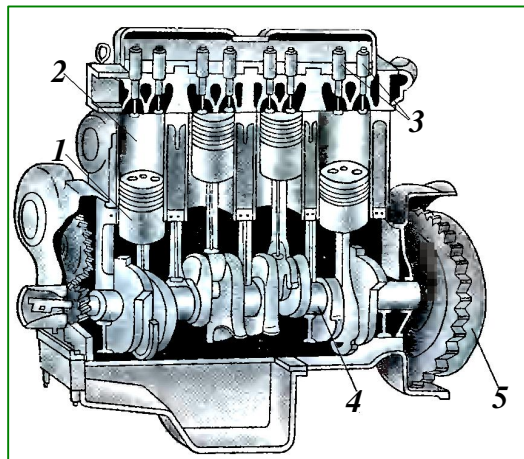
Современный автомобильный четырёхтактный четырёхцилиндровый ДВС, разрез: 1 – поршень; 2 – цилиндр; 3 – впускной и выпускной клапаны; 4 – коленчатый вал; 5 – маховик.
